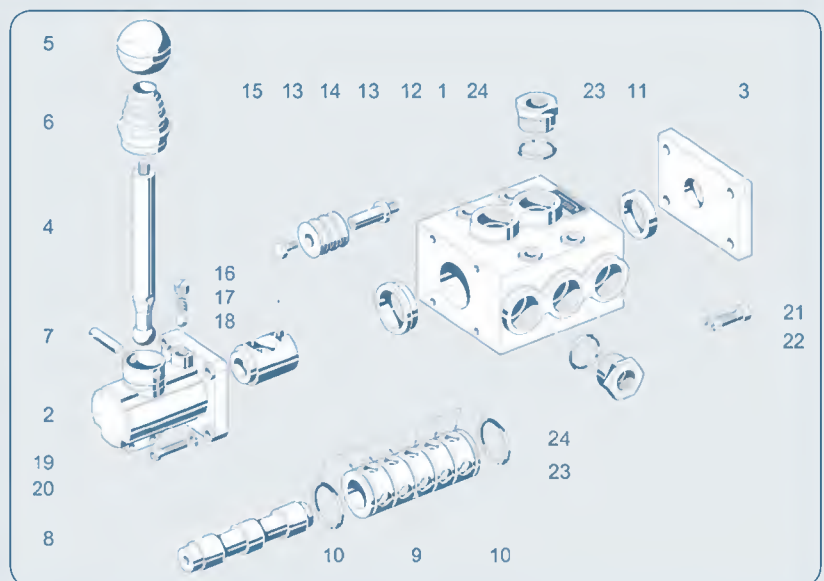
Explosionszeichnung zur Darstellung der einzelnen Komponenten
